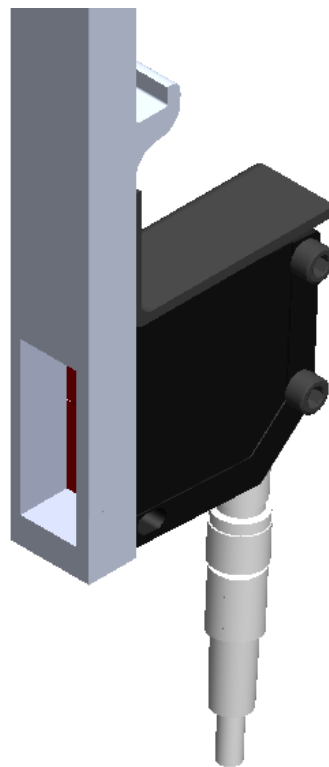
Vista isométrica. Diseño del montaje de sensor y tope.
